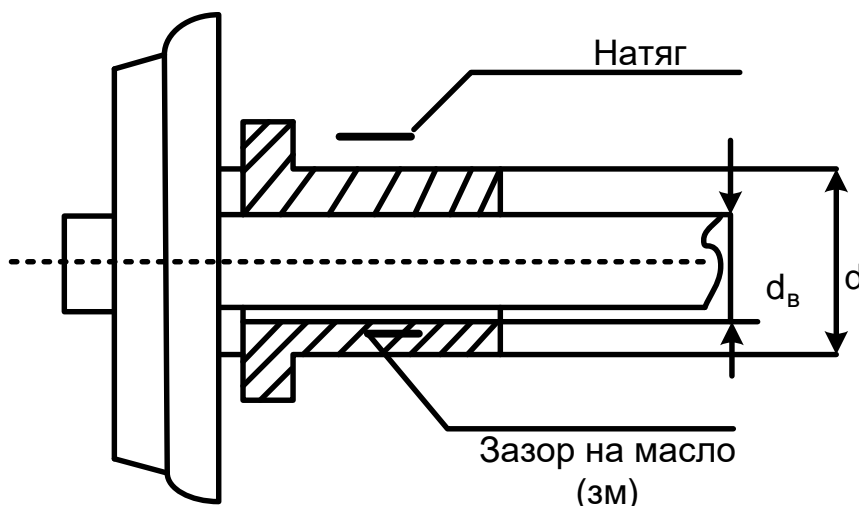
Схема установления пригоночного размера в моторно-осевом подшипнике
